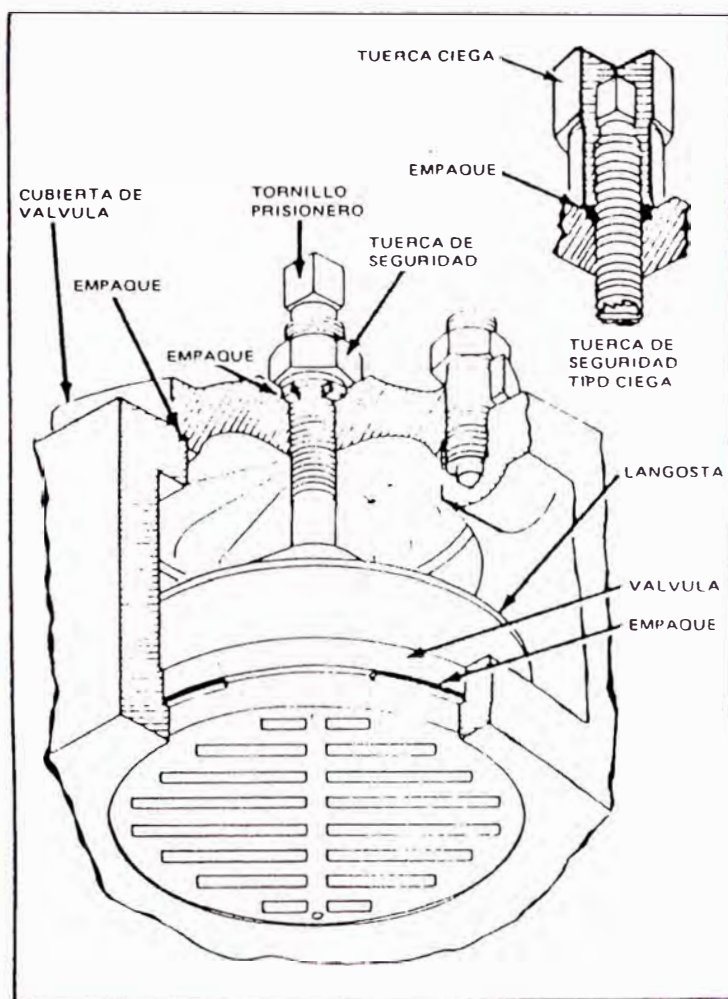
Disposición de la tapa y válvula de compresor de cilindros menores de 23 pulgadas de diámetro:
